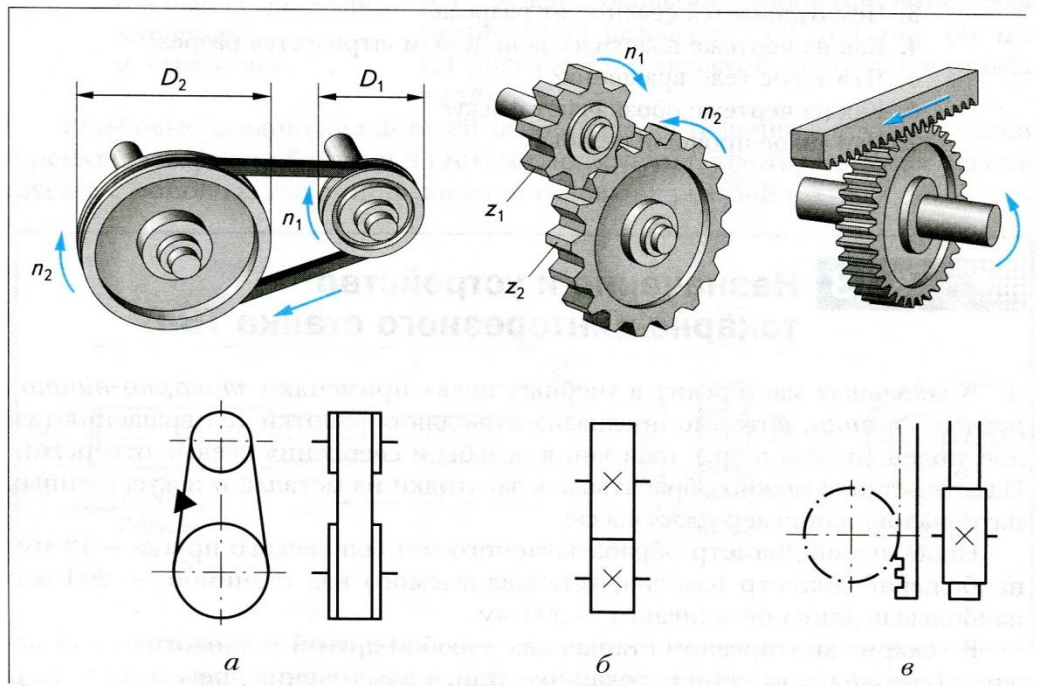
Виды механических передач, применяемых в токарном станке, и их условные обозначения: а — ремённая; б — зубчатая; в — реечная
